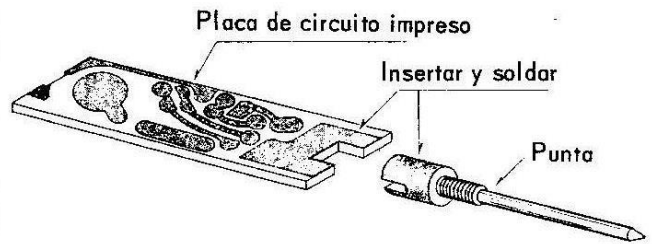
Montaje de la punta de prueba en el circuito impreso.
